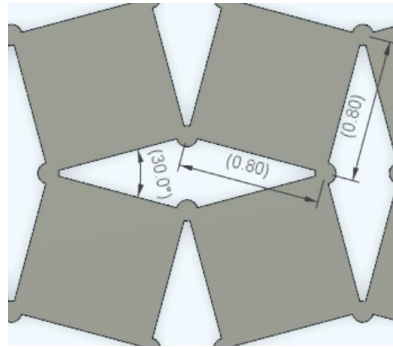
Detalles de la geometría de la estructura con cuadrados de lado 0,8 [mm] y ángulo de 30°.
